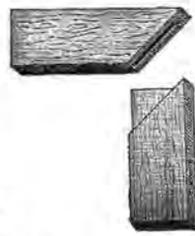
Assemblage d'onglet à tenon et mortaise.
